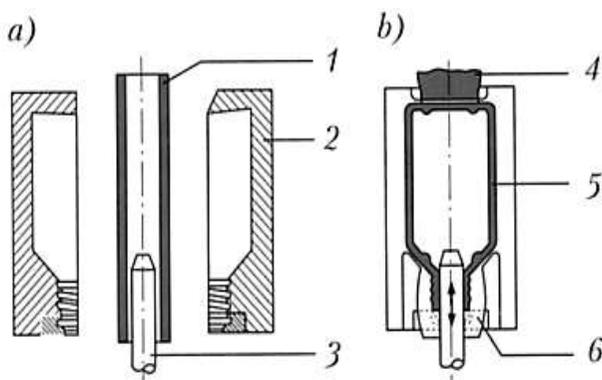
Раздувная форма с раздувным дорном: а – форма открыта; б – форма закрыта; 1 – рукав; 2 – форма; 3 – раздувной дорн; 4 – отжимной участок рукава; 5 – бутылка; 6 – калибровка горловины
